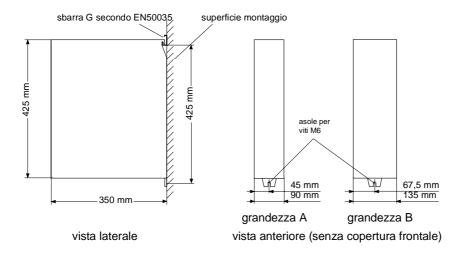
Disegni d'ingombro per montaggio grandezze A, B
